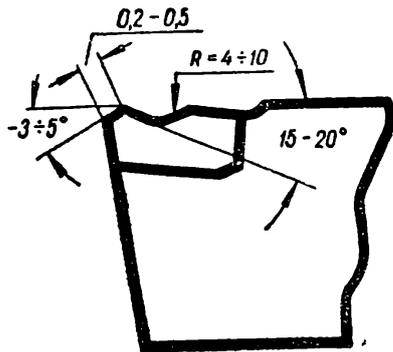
Твердосплавный резец с радиусной заточкой передней поверхности для ломания стружки.
